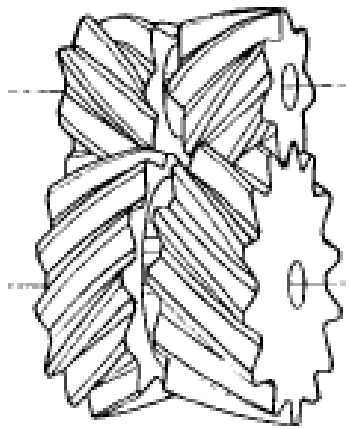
Engrenagem de eixos paralelos de dentado helicoidal duplo [2].
